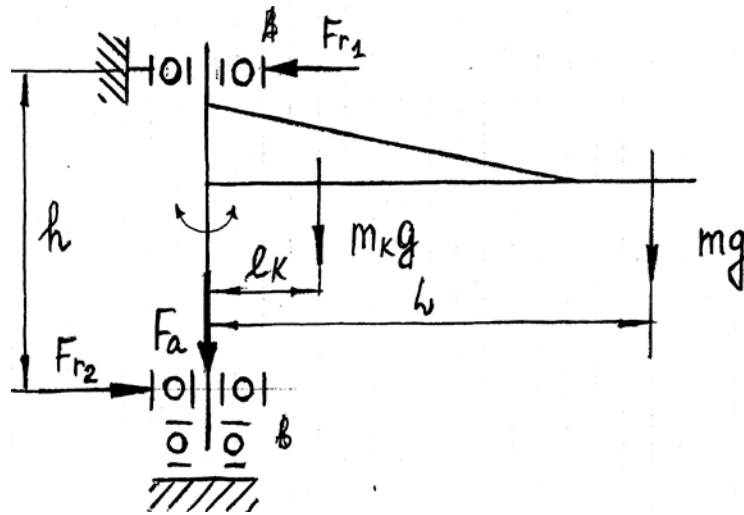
Расчетная схема крана с поворотной колонной.
